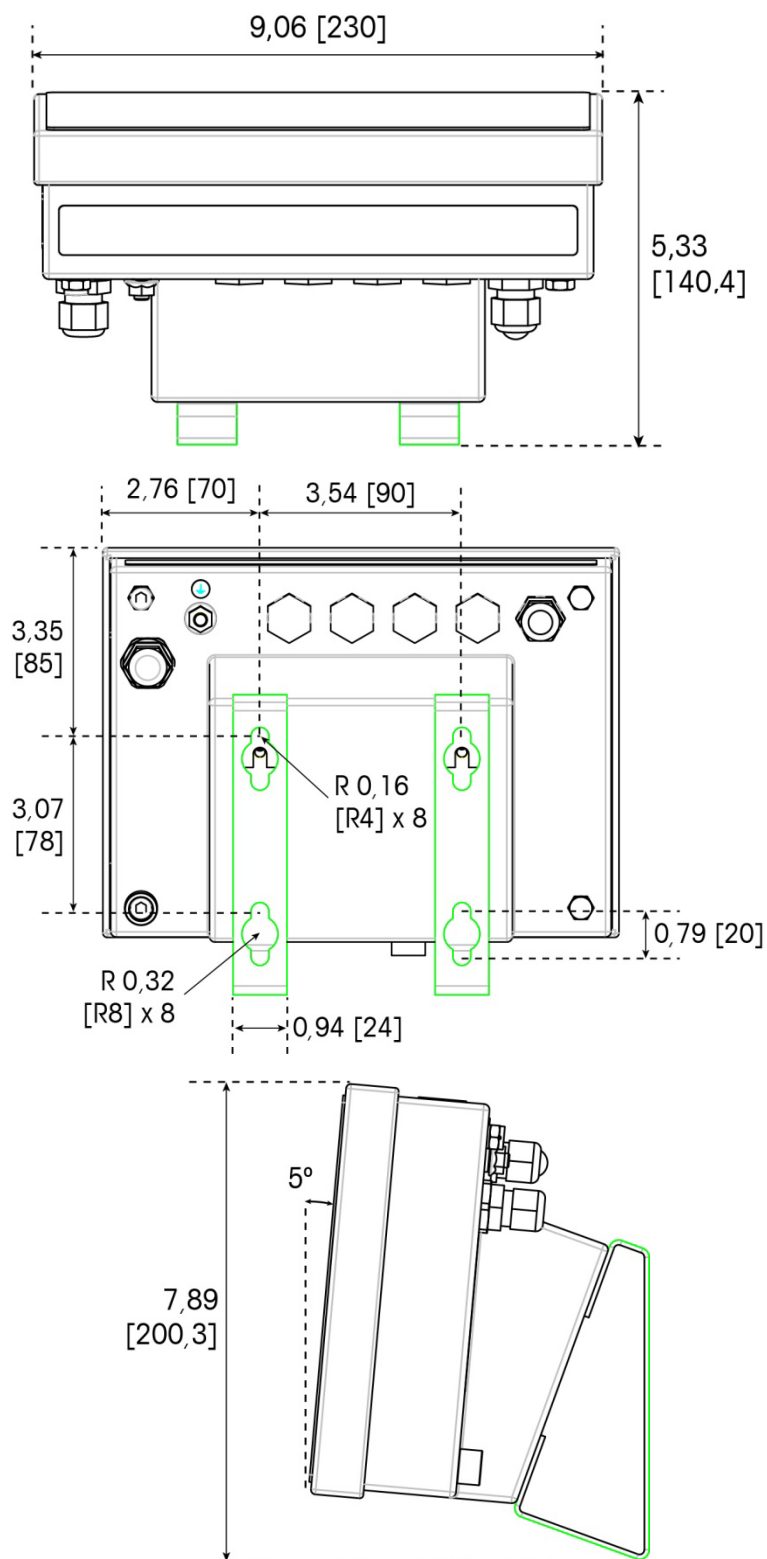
Dimensiones del IND256x, con soporte para montaje en pared
